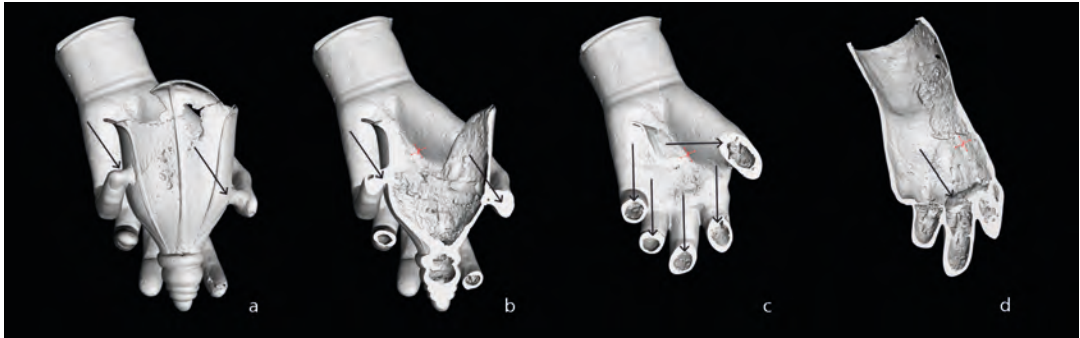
Computertomographie-Schnittbilder der vergoldeten Hand einer Monumentalstatue aus Bregenz (GBL 392–394). (a) Schweißpunkte zur Befestigung des Blütenkelchs; (b) Massiv angelegte Fingerpartien und Schweißpunkte sind aufeinander abgestimmt; (c) hohl gegessene Finger; (d) Sichtbare Wachsfügenaht und Wachsverlaufspuren der Fingermontage. Vorarlbergmuseum Bregenz.
